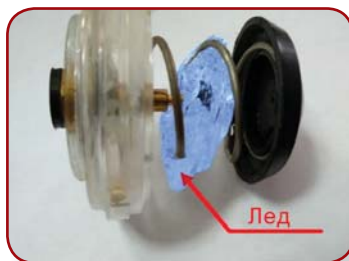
Большой кусок льда на пружине редуктора регулятора
